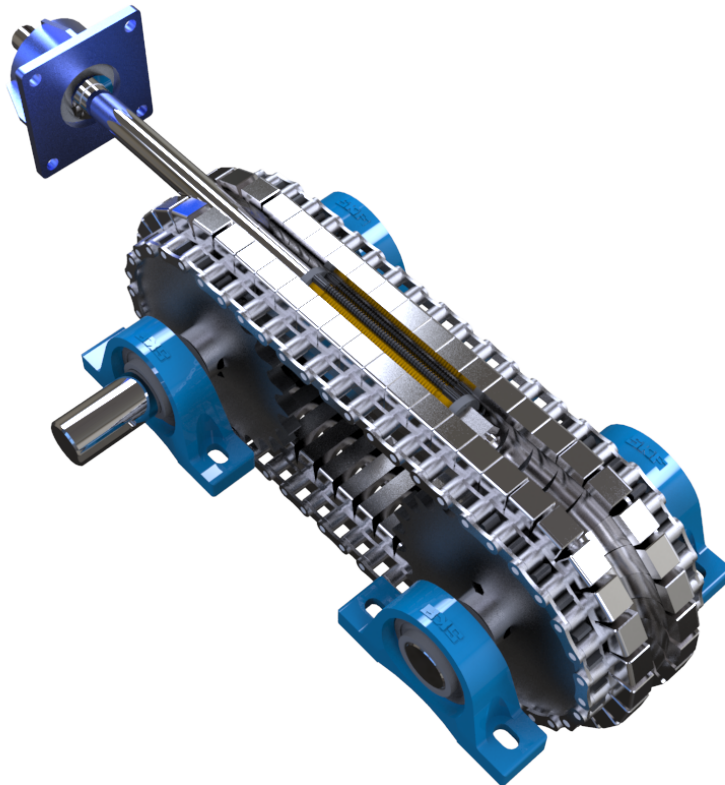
Vista del reductor con tornillo de rodillos y doble cadena
